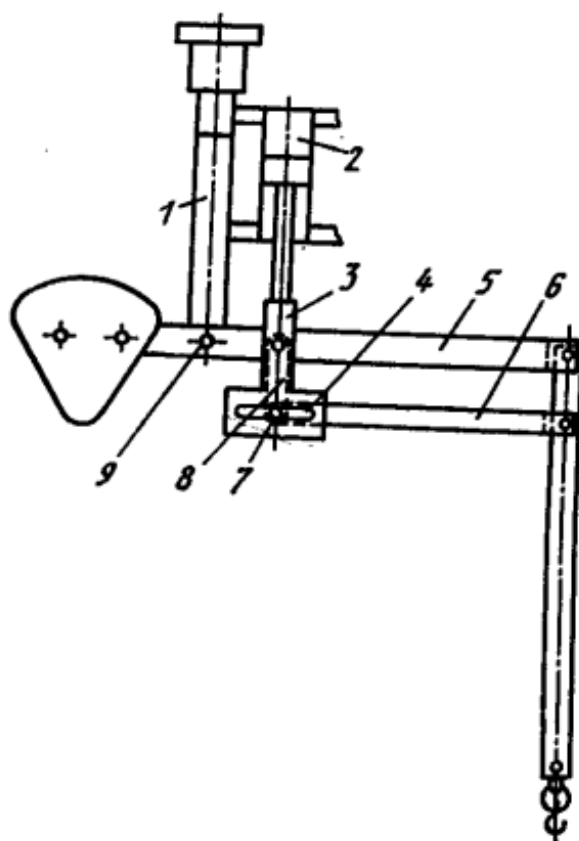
Схема збалансованого маніпулятора із приводом на поворотній колоні: 1 – поворотна колона; 2 – привод; 3 – Т-образна вилка; 4 – куліса; 5, 6, 8 – важелі; 7 – ролики; 9 – шарнір.
